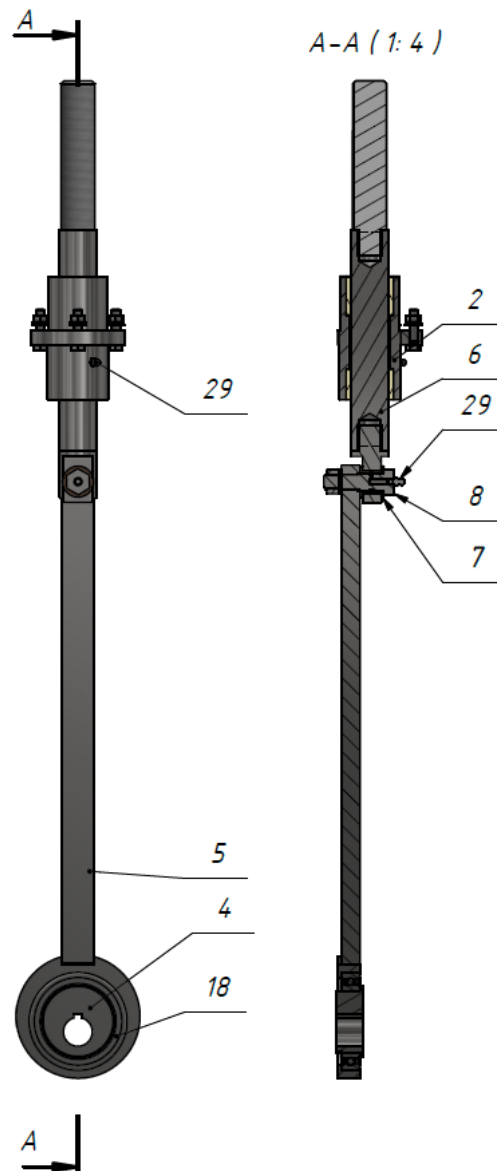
CAD модель механізму переміщення верхньої траверси
